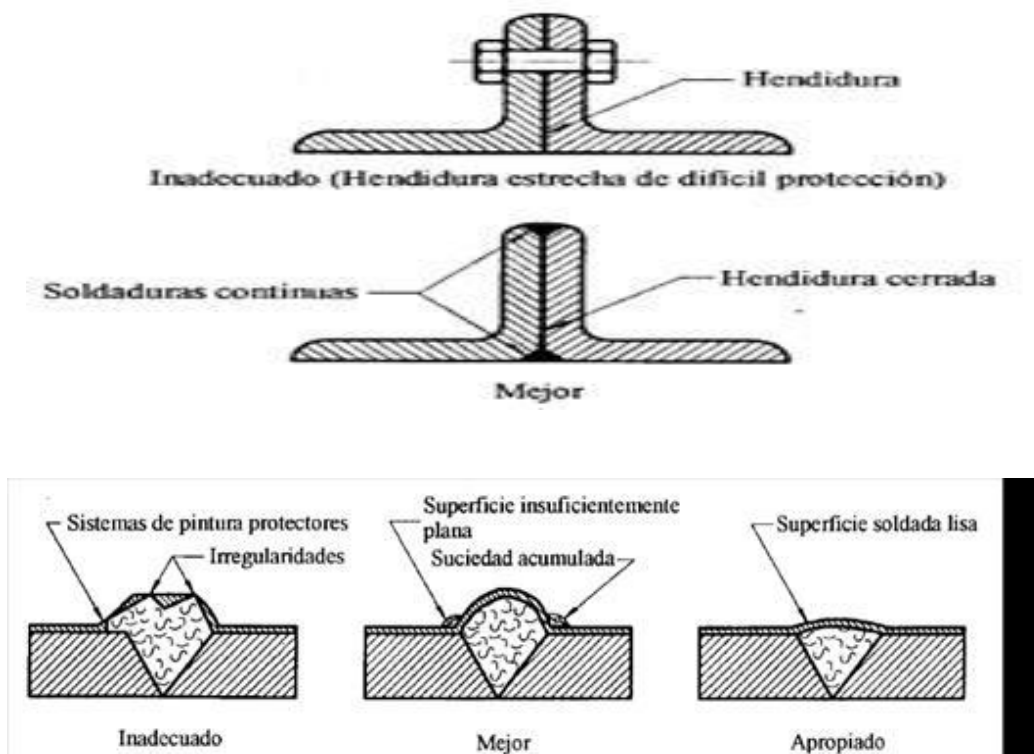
Eliminación de imperfecciones en la superficie de las soldaduras
